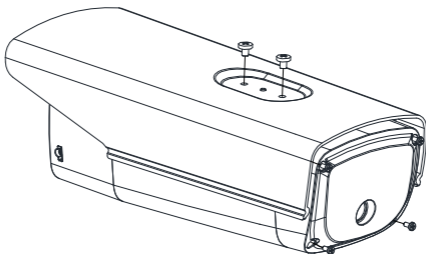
Установка задней крышки и солнцезащитного козырька
